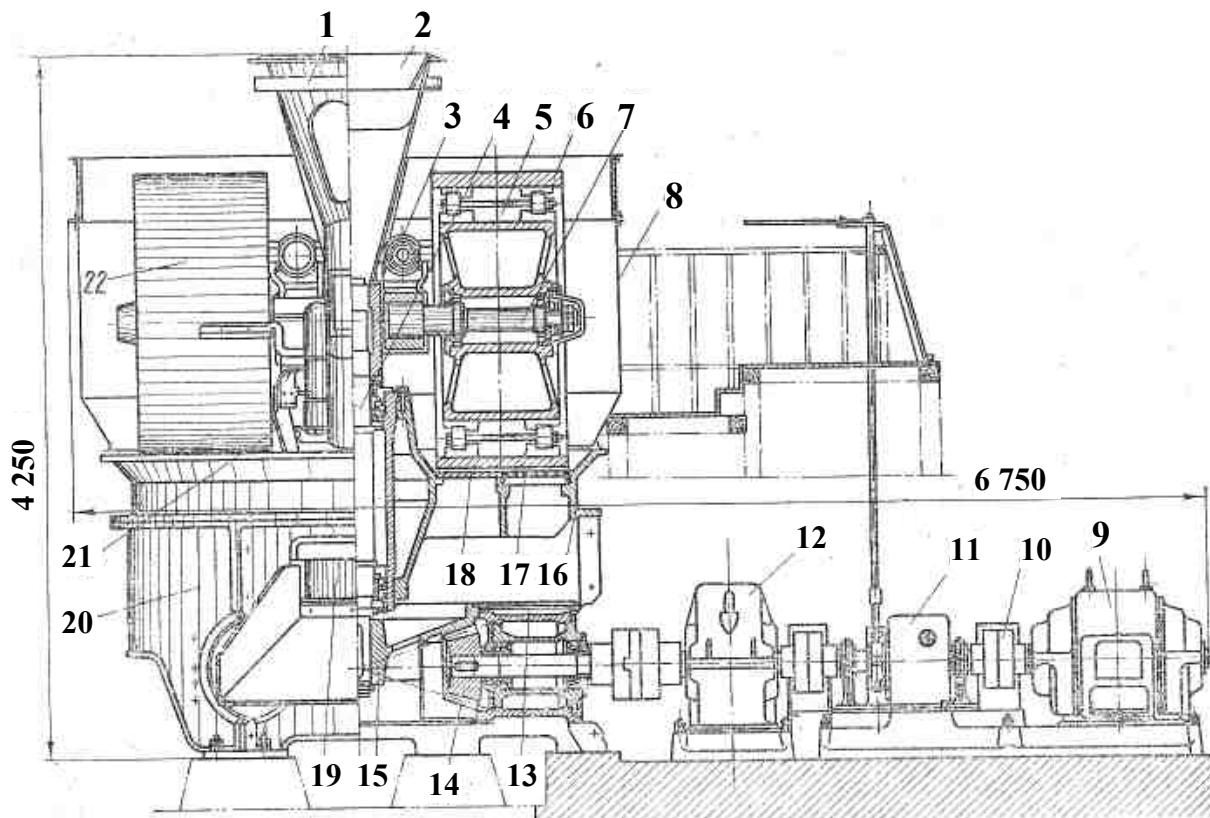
Бігуни мокрого перемелювання: 1 – таріль; 2 – обертальна піч; 3 – пружинний притискач; 4 – вертикальний вал; 5 – корпус котка; 6 – бандаж; 7 – колінчастий вал; 8 – кожух; 9 – електродвигун; 10 – вирівнювальна муфта; 11 – фрикційна муфта; 12 – редуктор; 13 – розвантажувальна таріль; 14, 15 – конічні шестерні; 16 – чаша; 17 – дірчаста плита; 18 – суцільна плита; 19 – розвантажувальний скребок; 20 – станина; 21 – очисний скребок; 22 – коток
